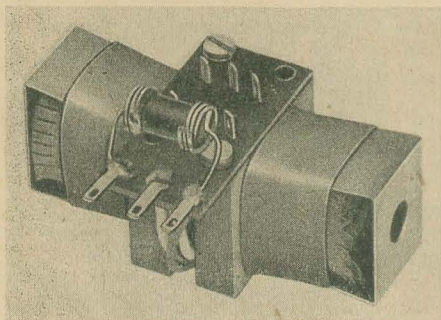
Ansicht des kompletten Magnetschalters mit NTC-Widerstand
